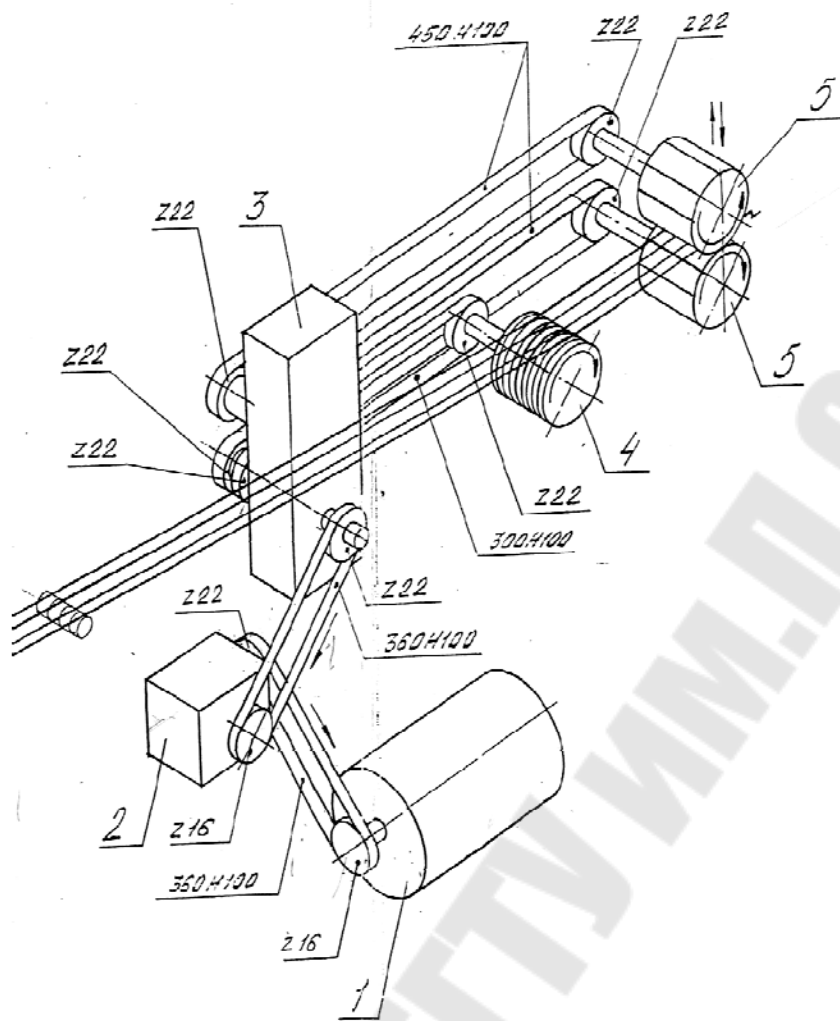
Принципиальная кинематическая схема станка для изготовления фибры:
